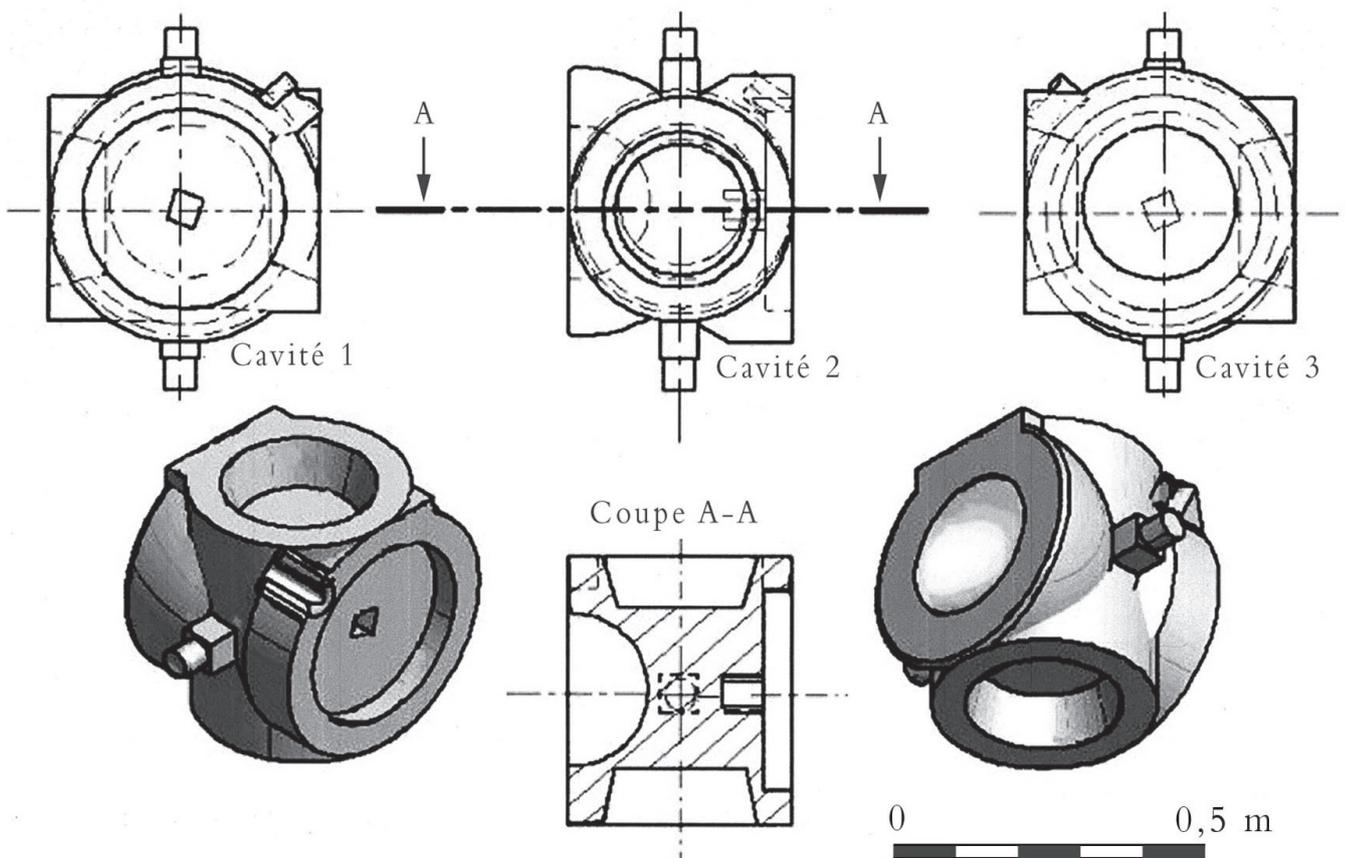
a : modélisation de la pierre de Sigy-le-Châtel (B.M)
